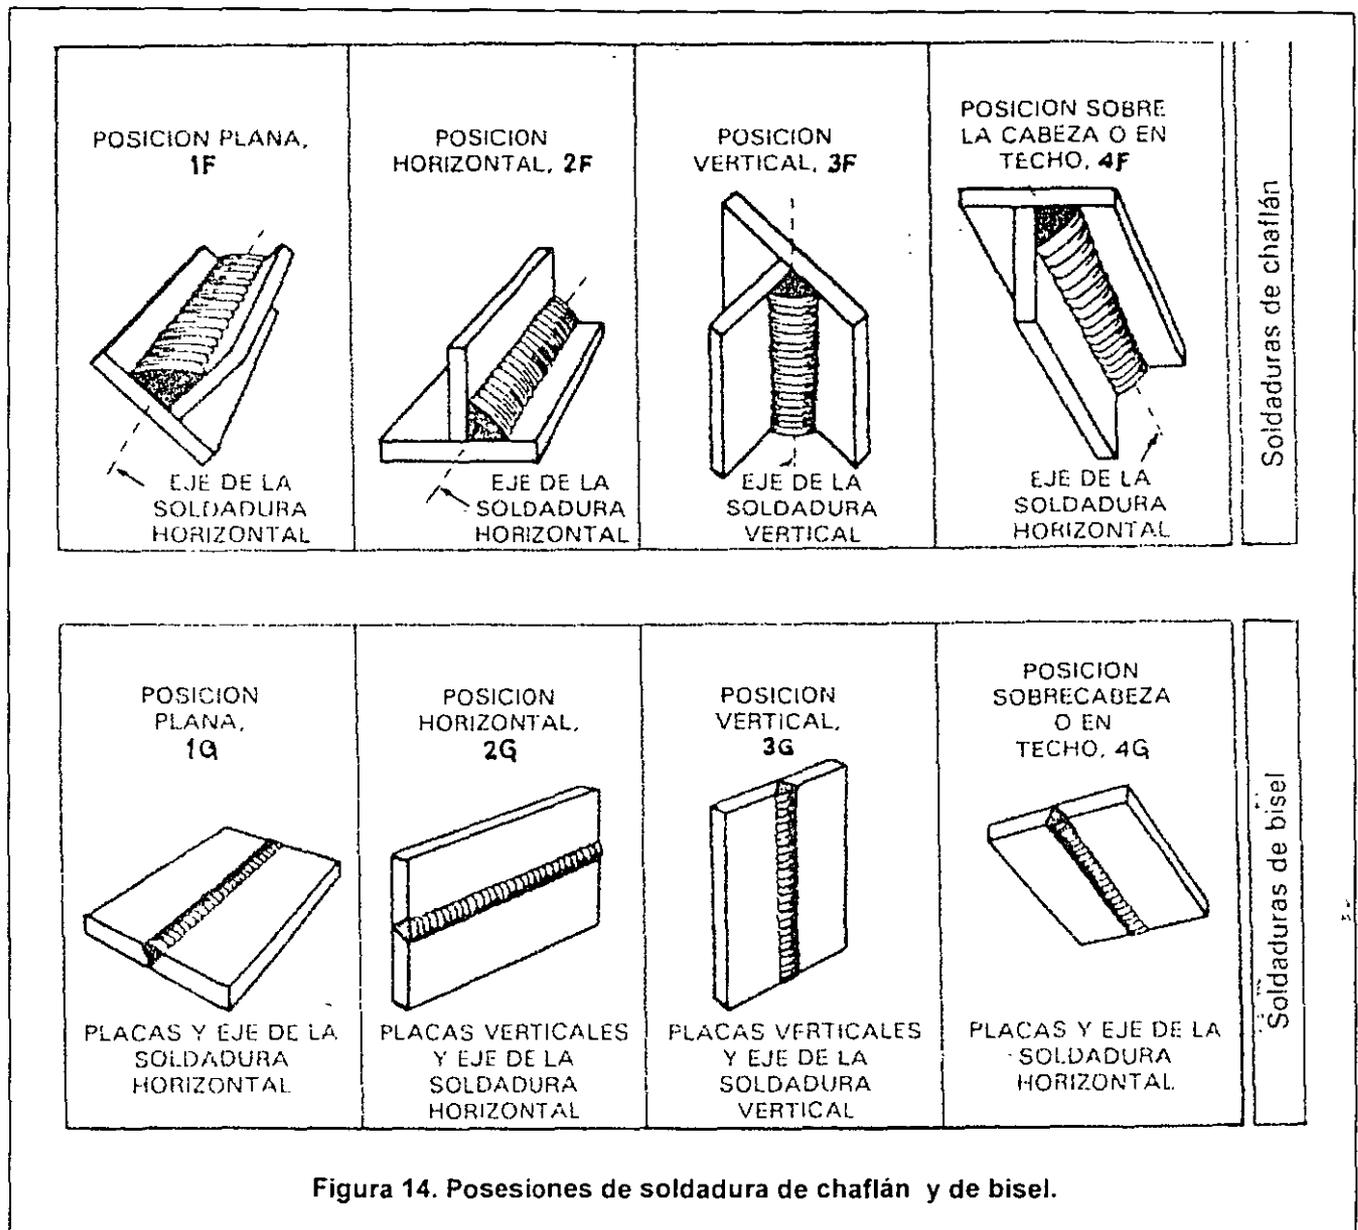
Posiciones de soldadura de chaflán y de bisel.
